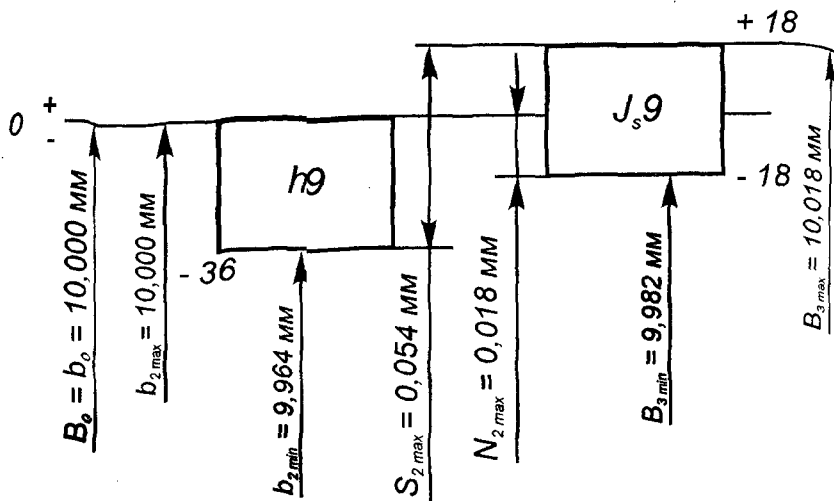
Схема расположения полей допусков ширины шпонки и ширины паза втулки
